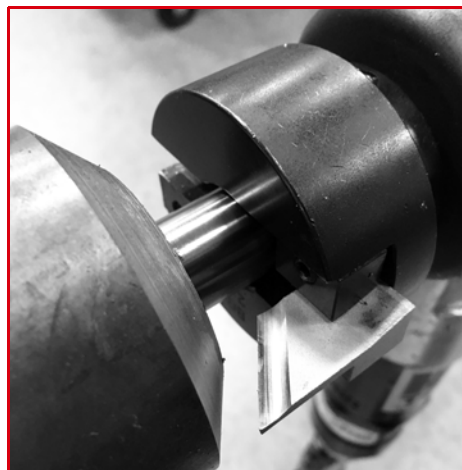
LAME DE COUPE INSTALLÉE
